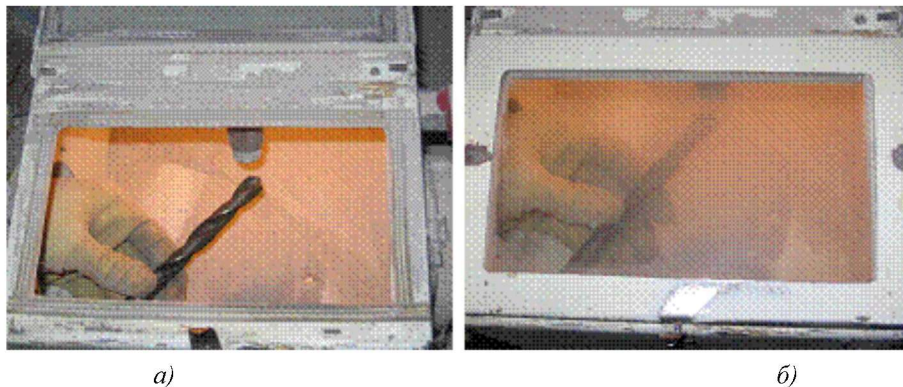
Общий вид устройства для пескоструйной обработки осевого лезвийного инструмента: а – общий вид зоны обработки; б – устройство в процессе работы
